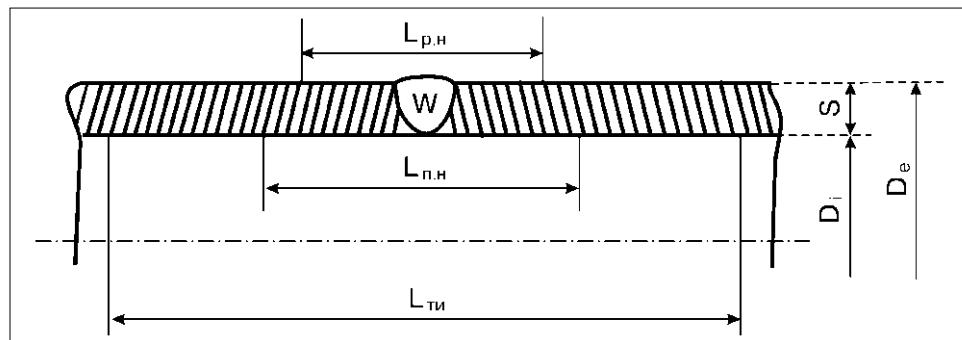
Расположение зон нагрева и установки теплоизоляции: D_i – внутренний диаметр трубы; D_e – наружный диаметр трубы; S – толщина стенки трубы; $L_{p.h}$ – зона полного нагрева; $L_{t.h}$ – зона установки теплоизоляции; W – ширина выпуклости (усиления) сварного шва
